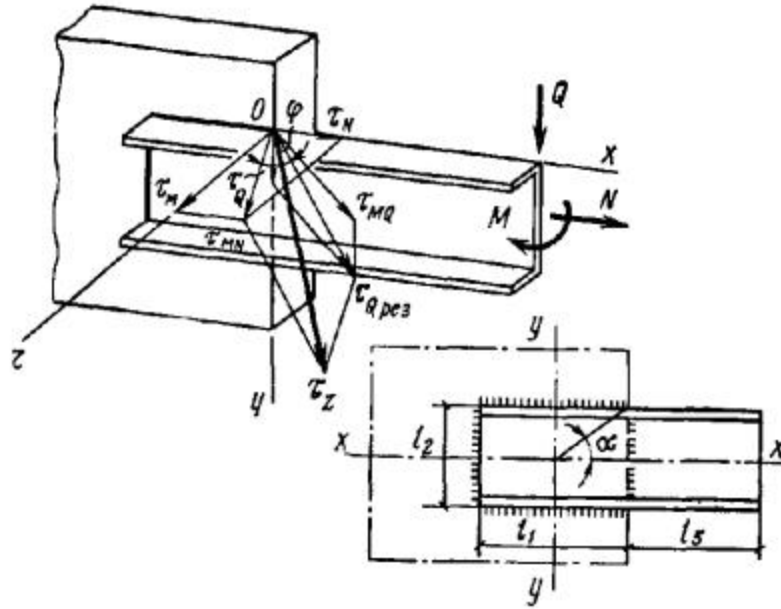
К расчету сварного соединения с угловыми швами на одновременное действие продольной и поперечной сил и момента
